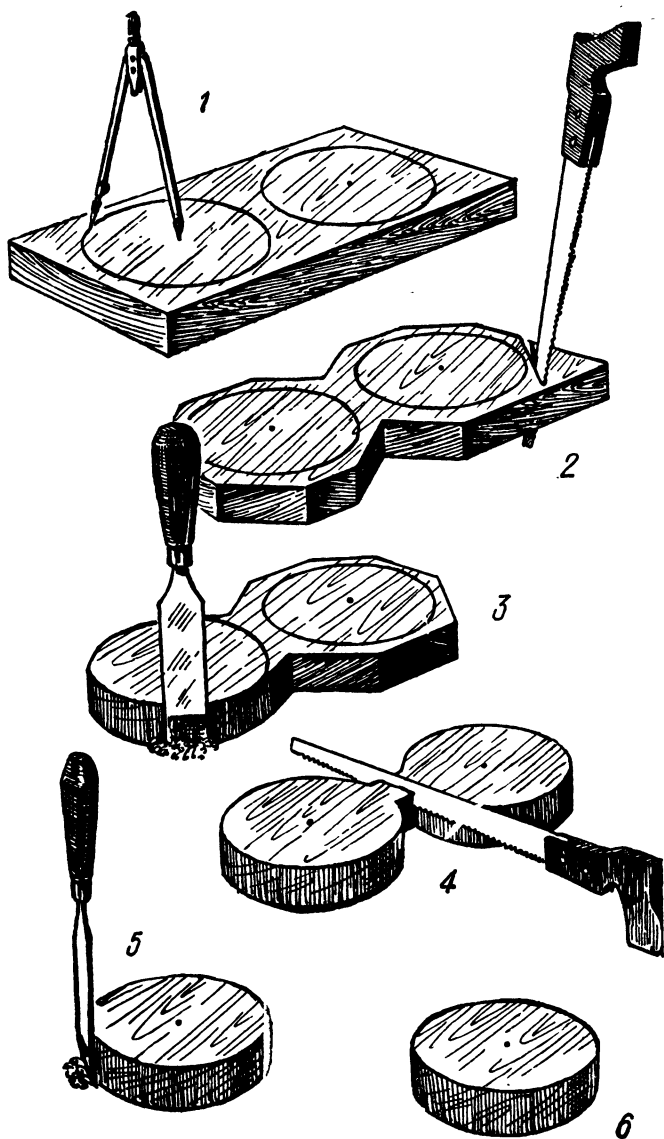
Изготовление колеса из доски (1—5 — последовательность обработки; 6 — готовое колесо).
